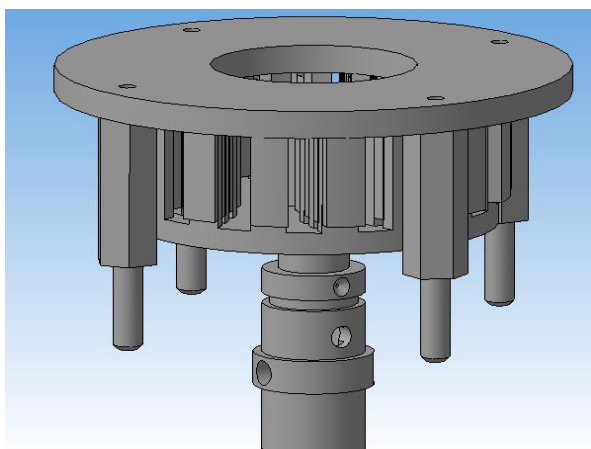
3D модель збирання ротора, статора і вала кавітаційного диспергатор-гомогенізатора
